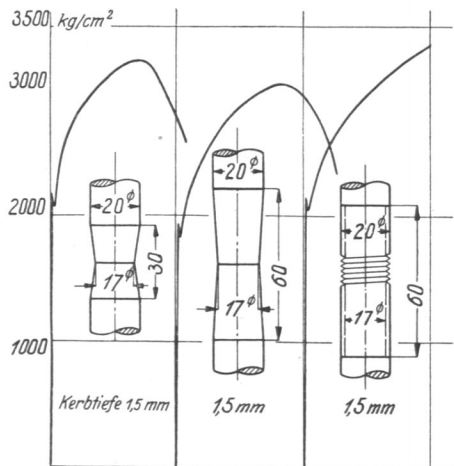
Zugversuche an schlank kegelig eingedrehten und mit Gewinde versehenen Flußstahlstäben.
